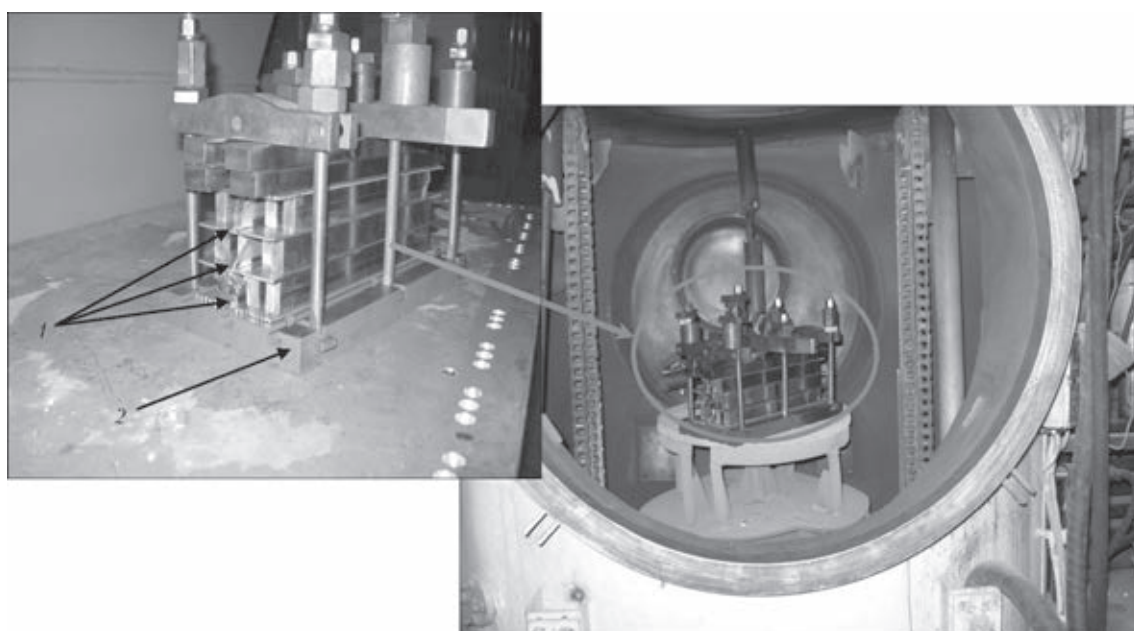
Термообработка сварных образцов из сплава ВТ20 в электровакуумной печи: 1 — тавровые образцы; 2 — оснастка для отжига в печи
